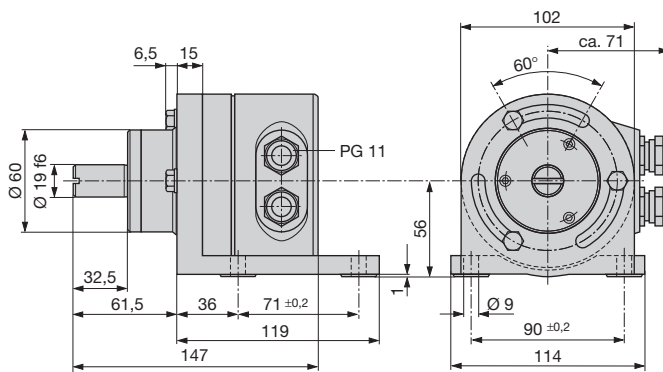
KINAX WT 707 mit Schraubklemmen sowie Stopfbuchsen und Fuss.
